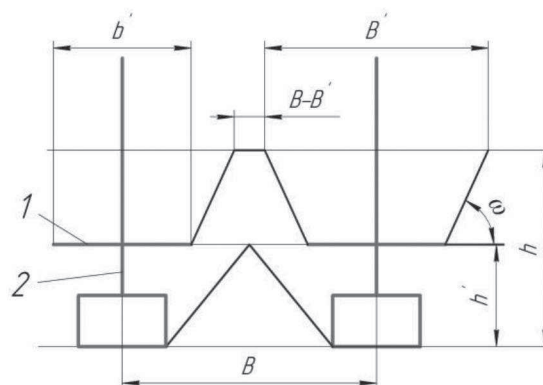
Расчетная схема для определения ширины боковых ножей: 1 – боковой нож; 2 – стойка
